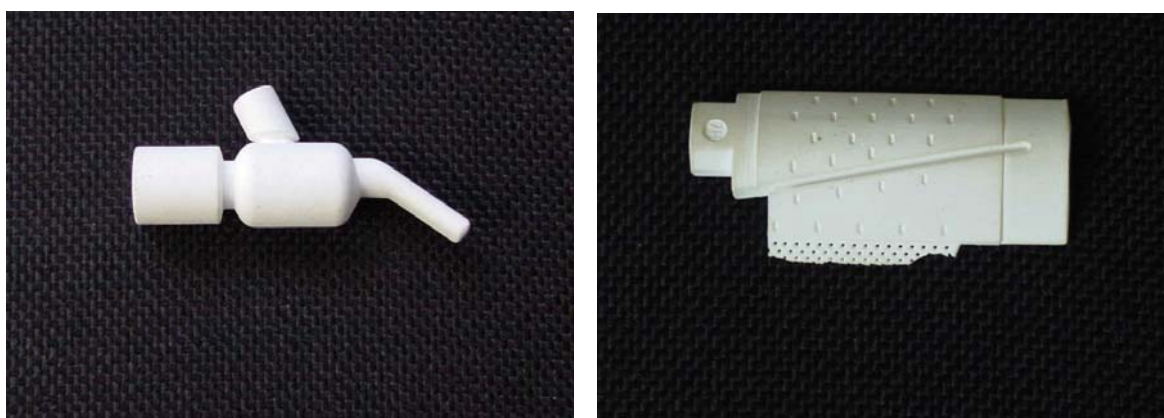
Macho cerâmico usado para fabricar bico injetor de motor a diesel (esquerda) e para formar caminho de resfriamento da palheta de turbina a jato (direita).
